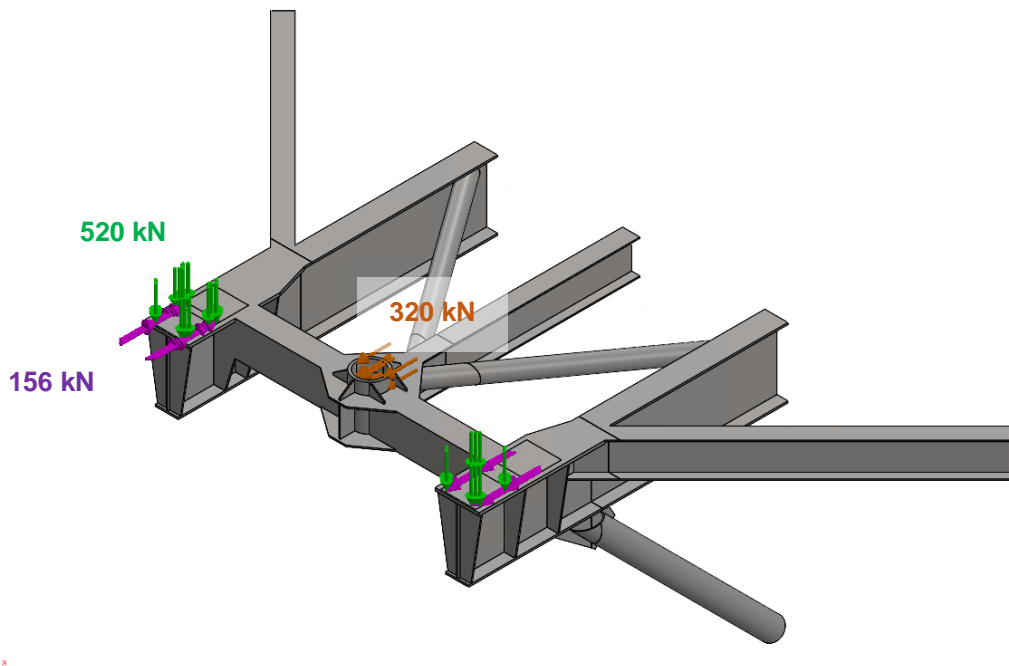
Lastaufbringung Gelenklager – Position 1
